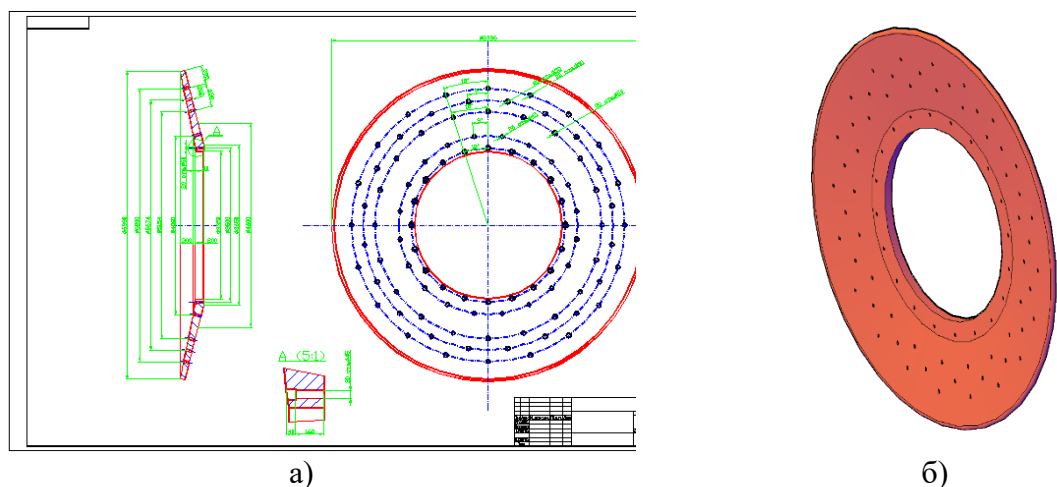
Креслення деталі: а) – креслення деталі; б) – об'ємна фігура типу SOLID.
